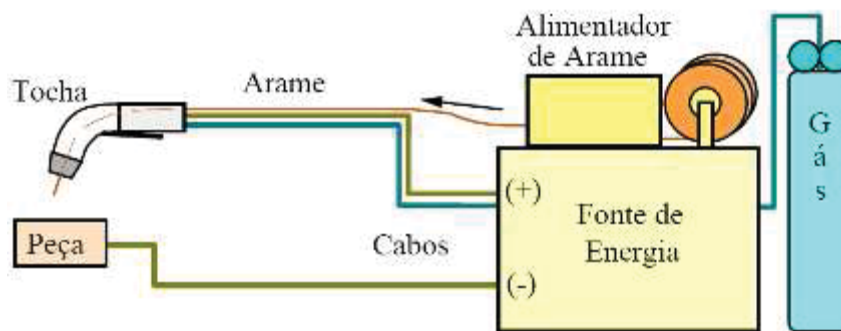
Equipamento de solda com arame tubular Bernados (Fonte: adaptada do catalogo ESAB)
